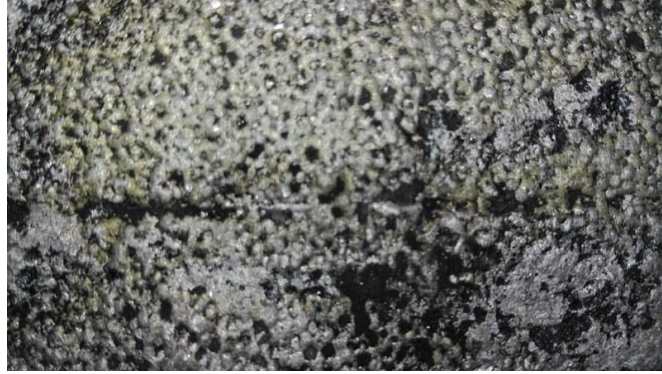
Grietas en la pieza proveniente de poliuretano.
